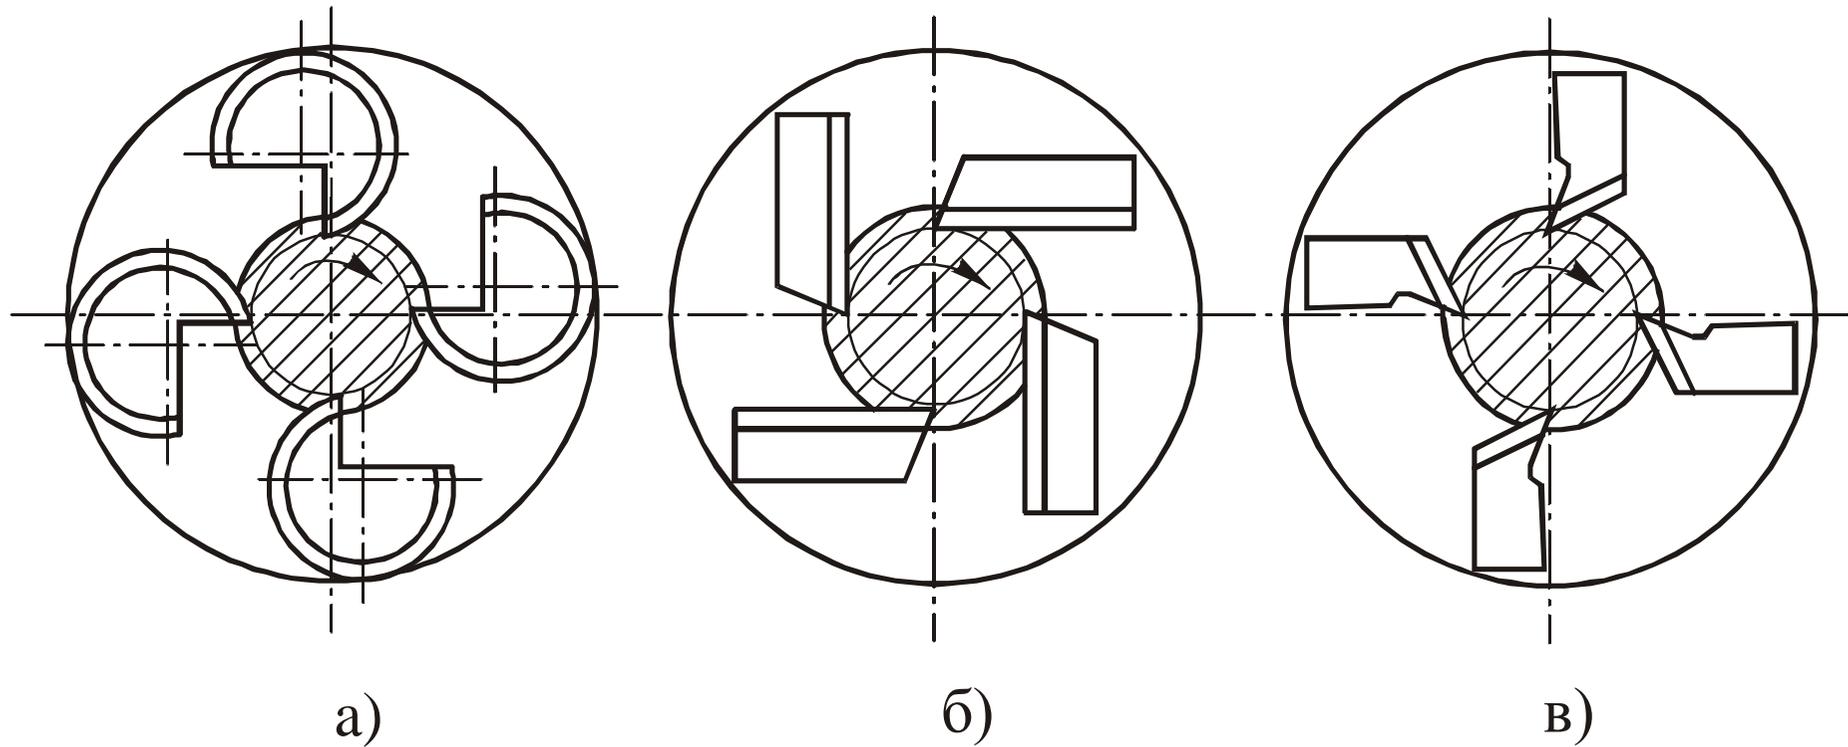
Типы резьбонарезных головок: *а* – с круглыми гребенками; *б* – с тангенциальными плашками; *в* – с радиальными плашками
